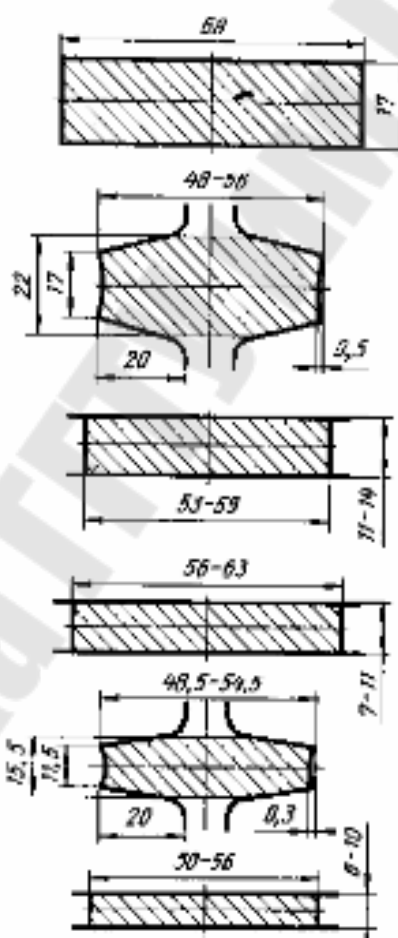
Схема отделочных калибров для полосового профиля (ход прокатки на схеме сверху вниз):
